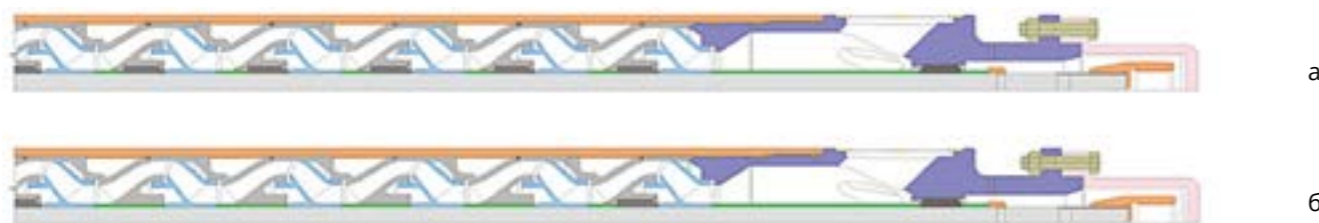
Варианты сборки подшипников: а – подшипник в каждой ступени; б – подшипник через каждые 5 ступеней
